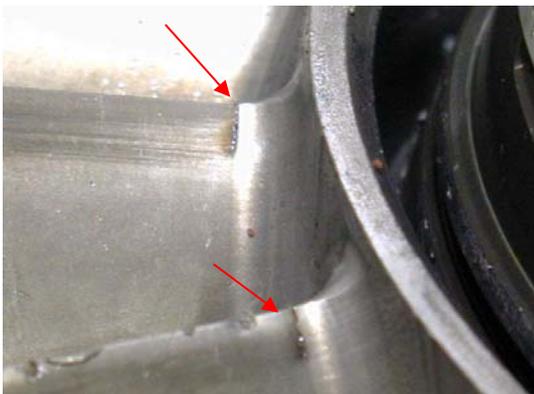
Brudd i kompressorblad. Motor S/N FA0016.
